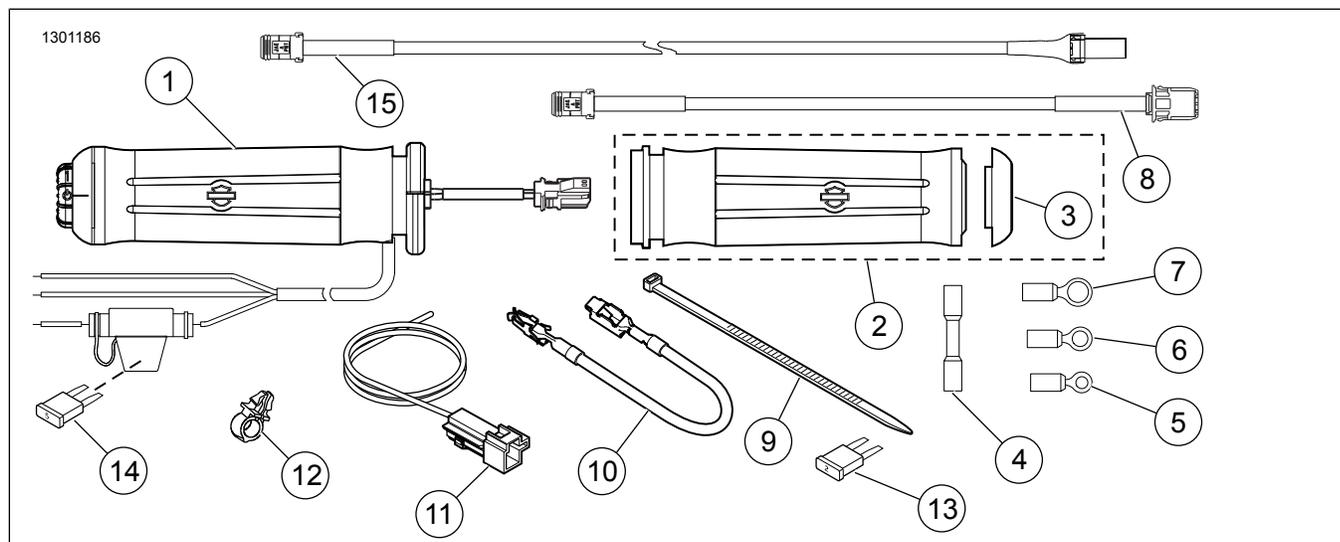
Piezas de servicio: Kits de empuñaduras con calefacción
